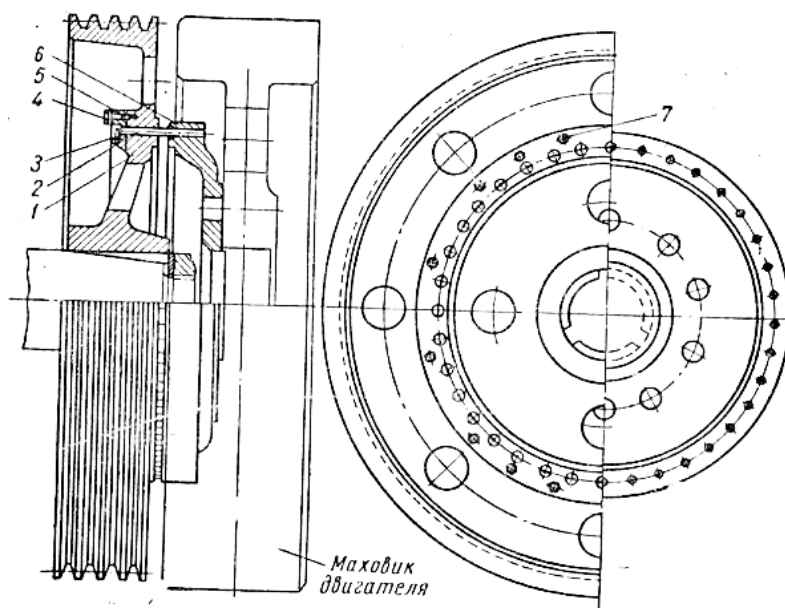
Конструкція муфти з пружними стрижнями пропульсивної установки
